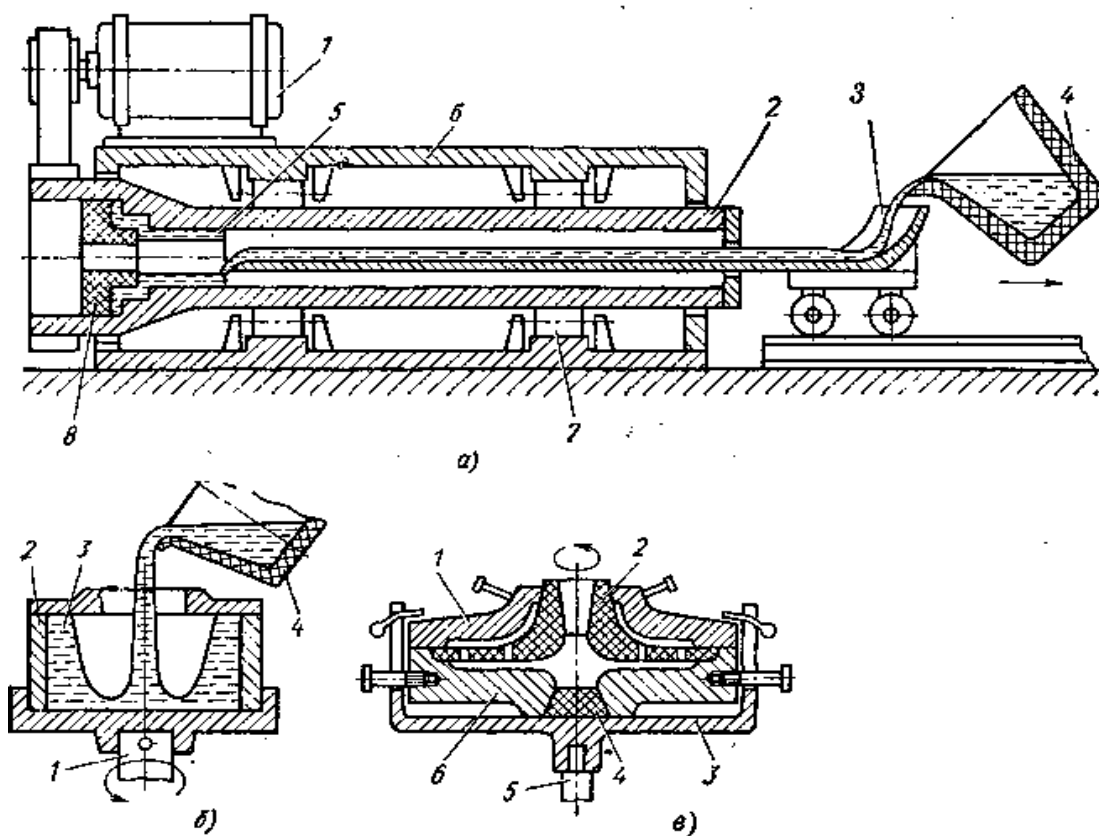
Схемы процессов изготовления отливок центробежным литьем.
